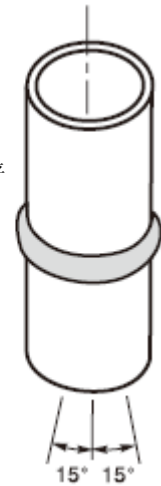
焊缝的试验位置（参见 4.1.9）
